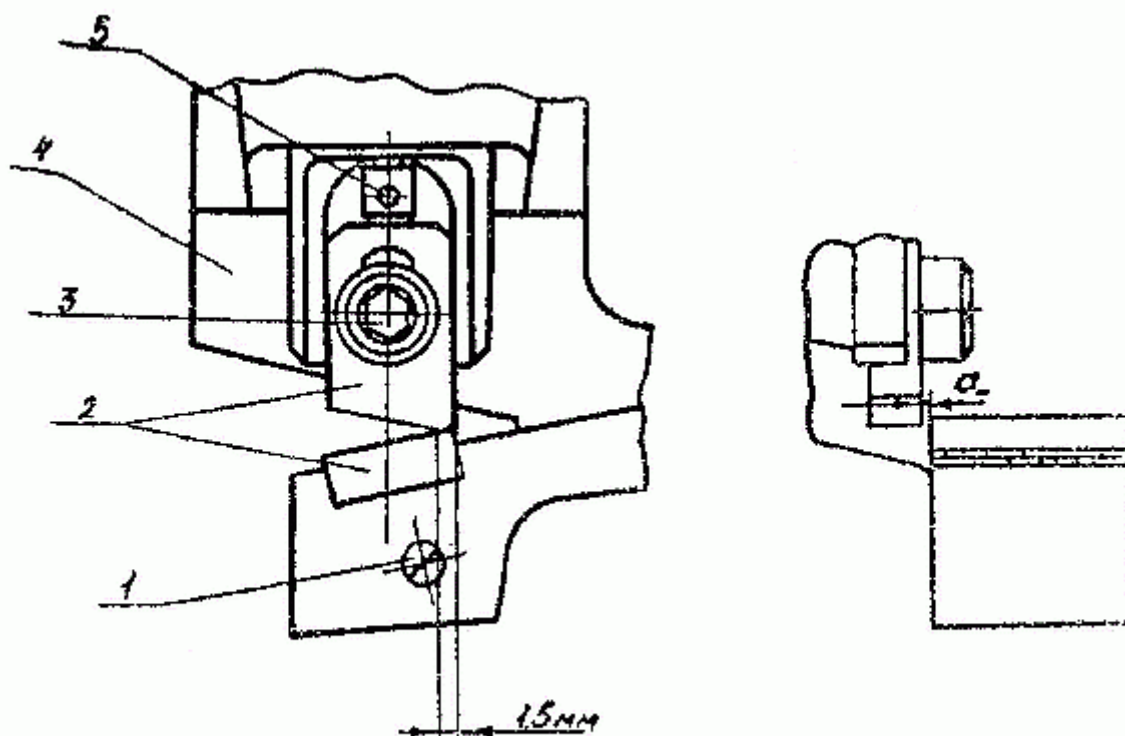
Правильная установка ножей: 1, 5 — винты регулирующие; 2 — ножи; 3 — винт; 4 — держатель ножа.
